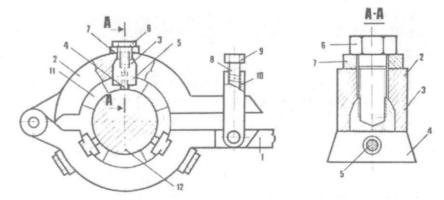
Схема устройства Д.91 для ФАБО коленчатых валов: 1 — корпус; 2 — щеки; 3 — державки; 4 — натирающие инструменты; 5 — фиксатор; 6 — винты; 7 — подшипник скольжения; 8 — регулировочный винт; 9 — гайка; 10 — пружина; 11 — тампон; 12 — деталь
